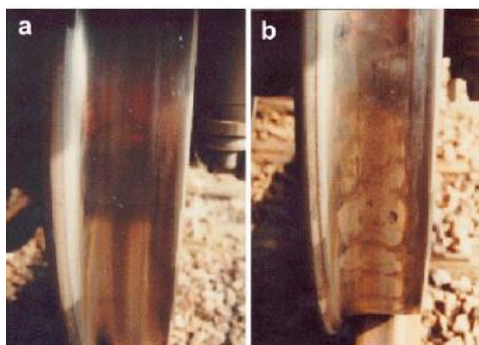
Superfície de rolamento de roda com (a) sistema de frenagem de discos, (b) sistema de frenagem de cepos atuantes na roda.
